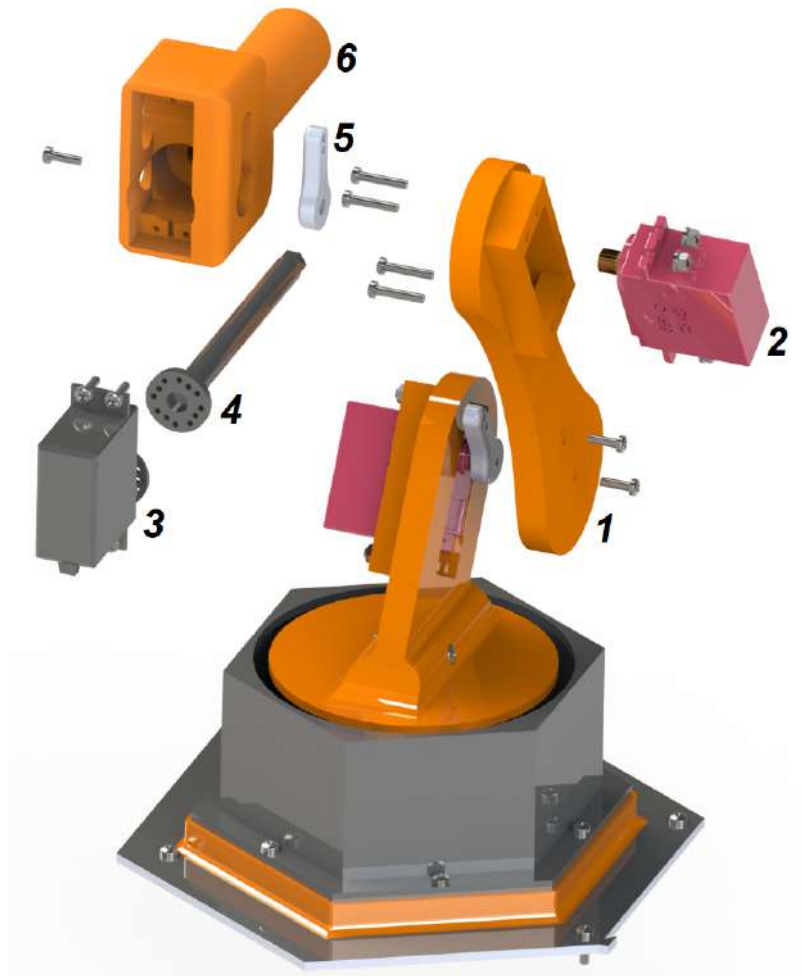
CAD de vista explosionada para ensamble del 2.do,3.er y 4.to gdl.
